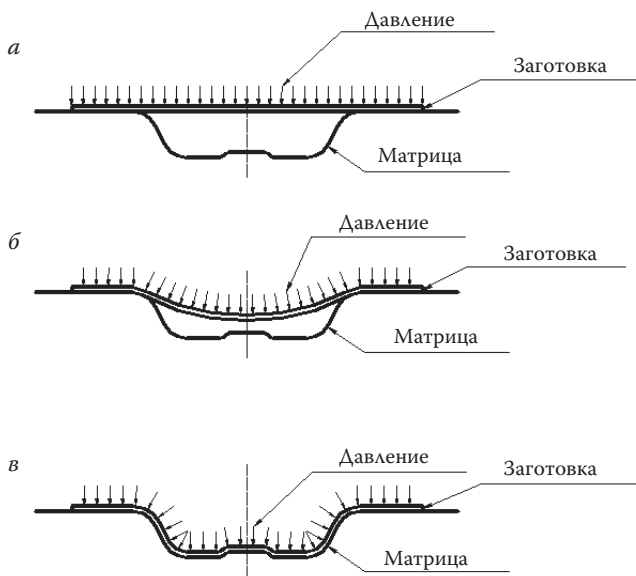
Схема формообразования способом пневмотермической формовки («формовка»)
